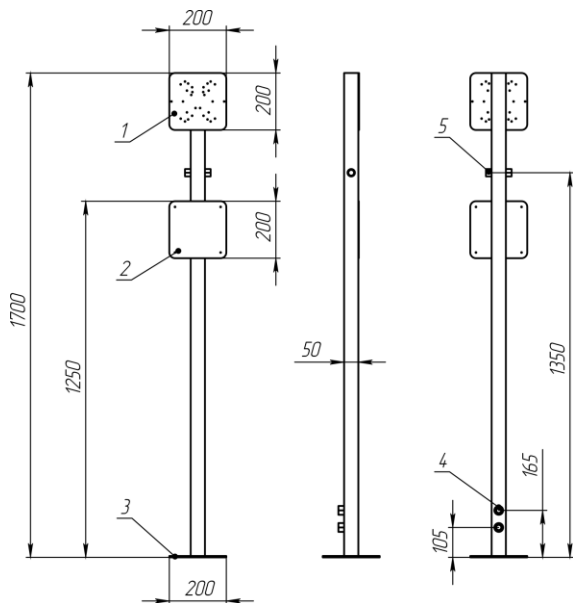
Внешний вид и габаритные размеры стойки пожарной СП-01
